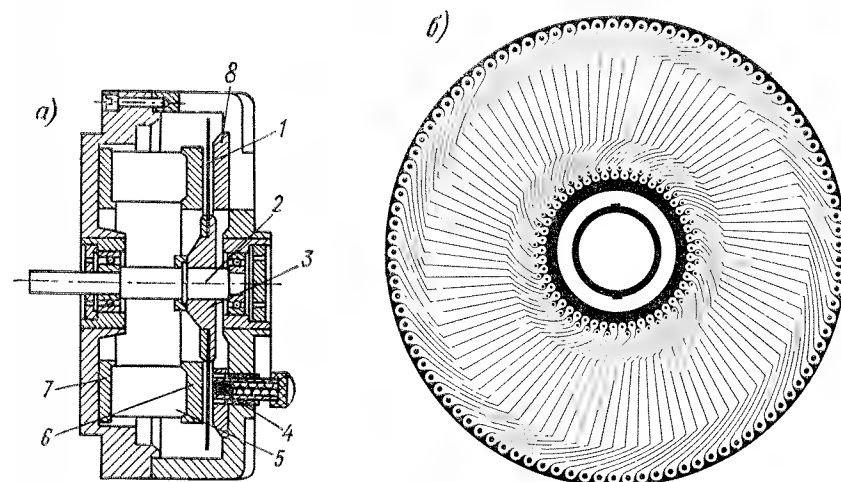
Двигатель постоянного тока с печатной обмоткой якоря: а — разрез двигателя; б — обмотка якоря
